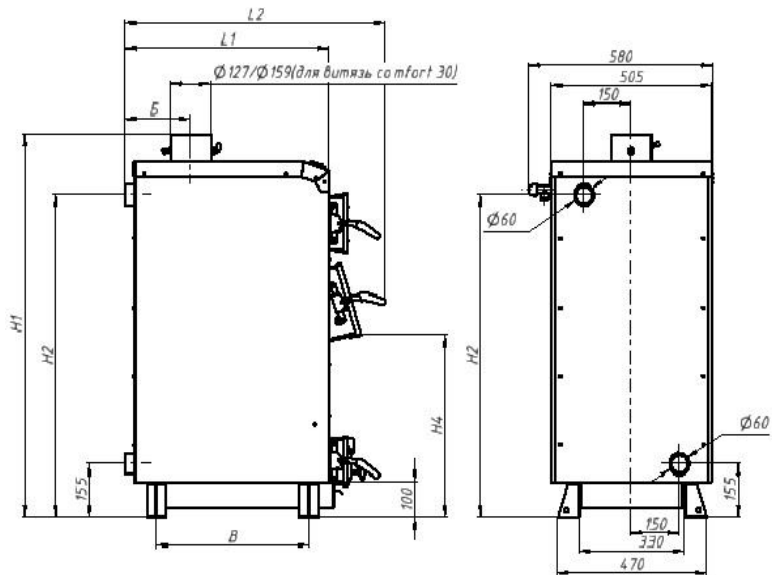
Установочные и габаритные размеры котла Витязь Comfort.
